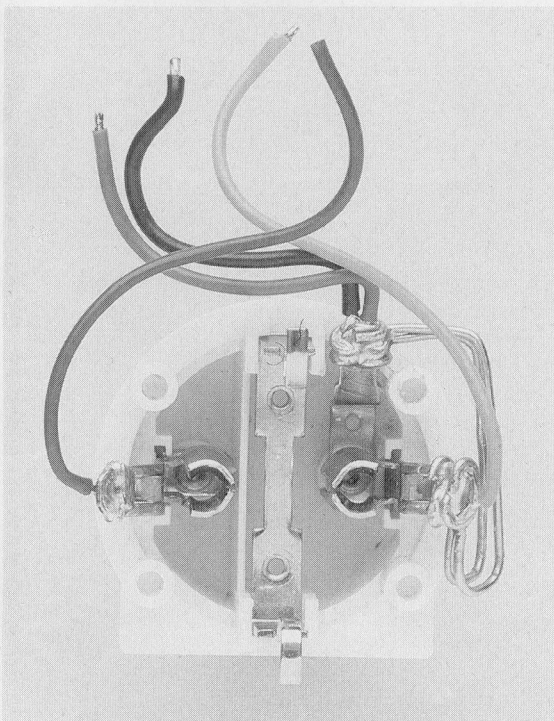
Cette photographie illustre, mieux que mille mots, la technique de mise en place et de soudure des 2 fils résistifs et des 4 conducteurs d'interconnexion.
